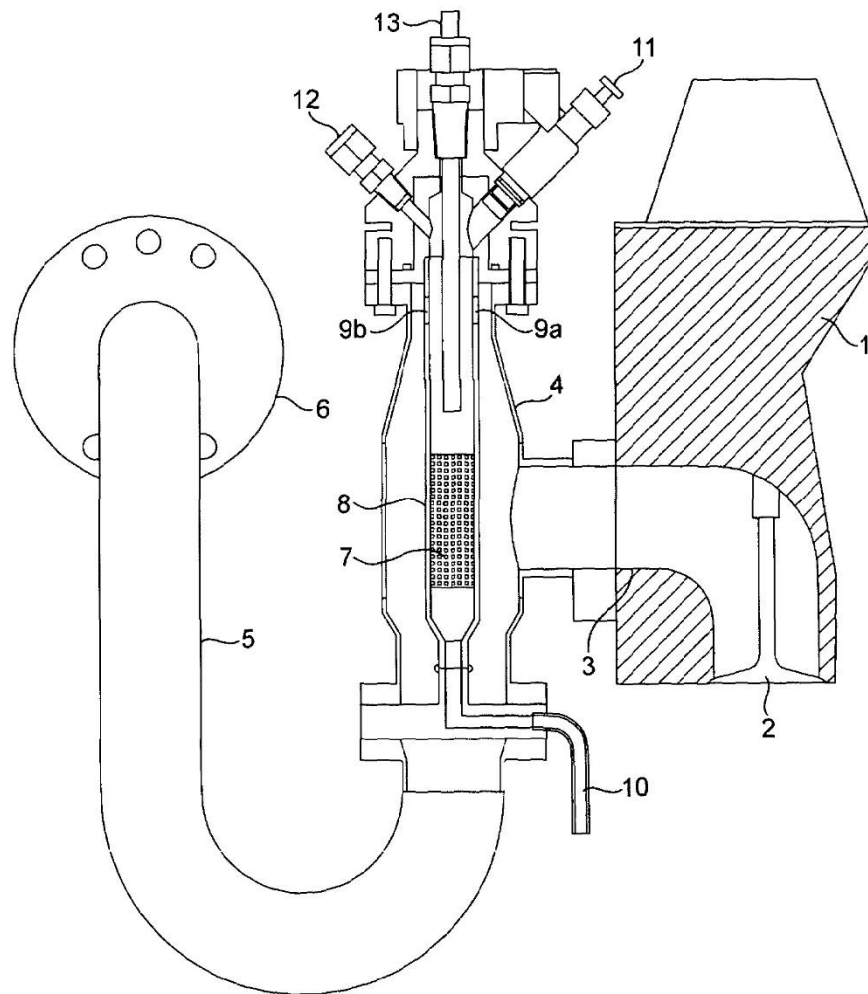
Схема установки реформінгу палива: 1 – головка блоку циліндрів; 2 – впускний клапан; 3 – випускний отвір; 4 – впускний отвір; 5 – вискна труба; 6 – турбокомпресор; 7 – каталізатор; 8 – кільцевий корпус; 9 a,b – впускні отвори; 10 – випускна труба; 11 – засіб подачі дизельного палива; 12 – вхідна точка термопари; 13 – пусковий підігрівач
